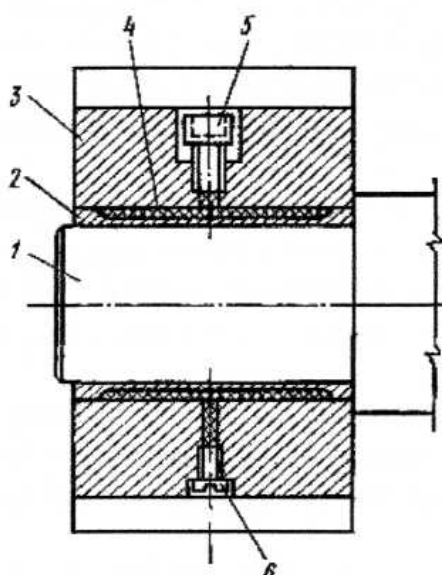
Схема гидропластмассового закрепления фрезы на шпинделе:
